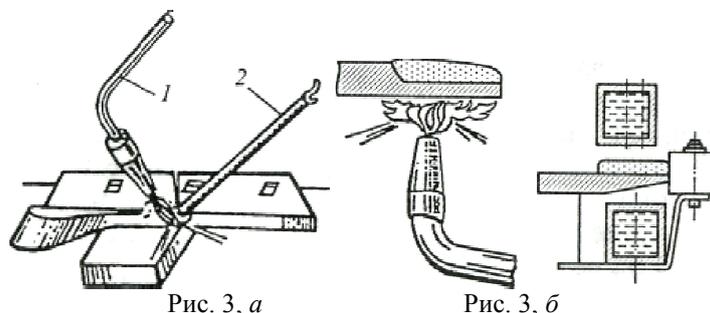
Способы нагрева лезвия плужного лемеха при наплавке твердого сплава: *a* – прямой нагрев прутка из твердого сплава сормайт № 1 газовой горелкой; *б* – нижний нагрев лезвия лемеха с насыпной шихтой; *в* – нагрев ТВЧ; *1* – горелку; *2* – прутки из твердого сплава
